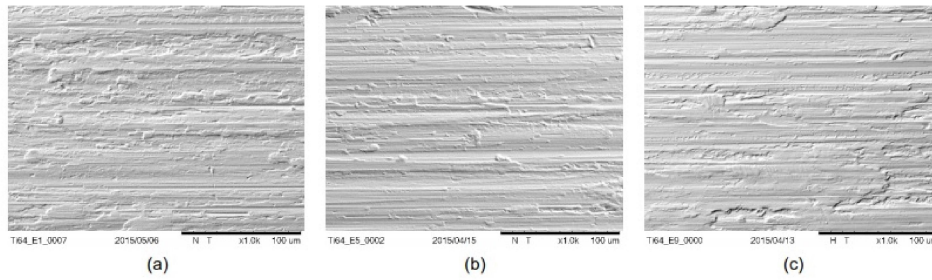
Imagens de MEV, ensaios com penetração de trabalho de  $10 \mu\text{m}$ , 2 passes, utilizando (a) técnica convencional; (b) técnica MQL e; (c) técnica MQL com adição de grafeno.
